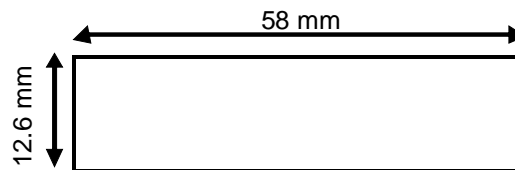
Dimensiones de las probetas para pruebas mecánicas
